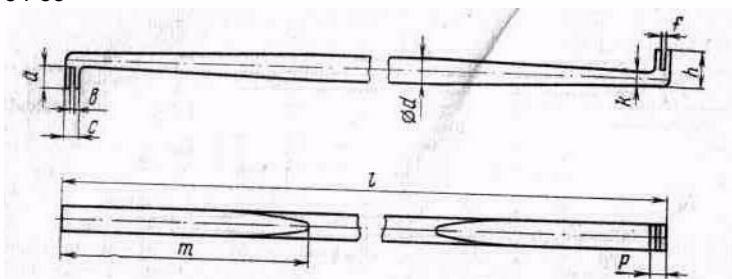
Инструмент для регулировки реле КДР, НШ, НМШ, НПШ1-150, НМПШ, АШ
